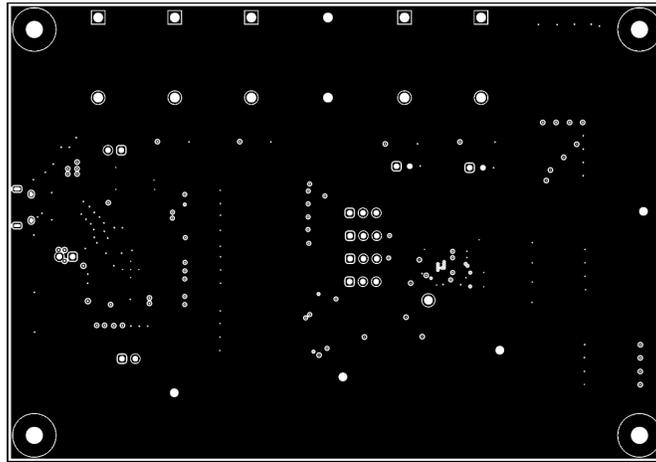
AMC6V704EVM PCB 中层 1 布局 ( 接地平面 )
